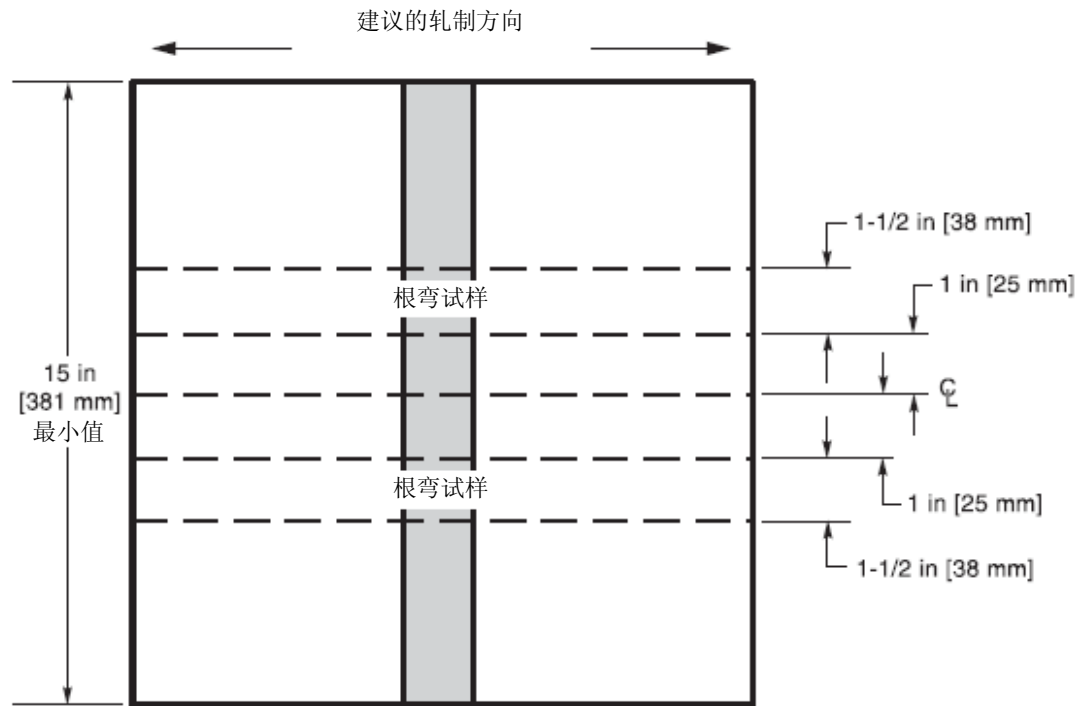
管材 (有衬垫) 对焊接头 — 焊工资格评定用
